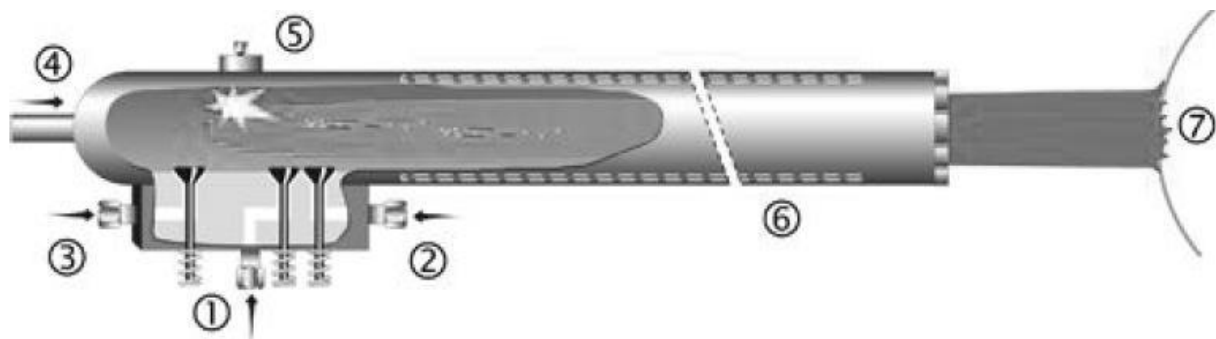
Схема детонаційного напилення покриття: 1 – ацетилен; 2 – кисень; 3 – азот; 4 – напилюваний порошок; 5 – запалювальний пристрій; 6 – охолоджувана вихідна труба; 7 – деталь [2].
